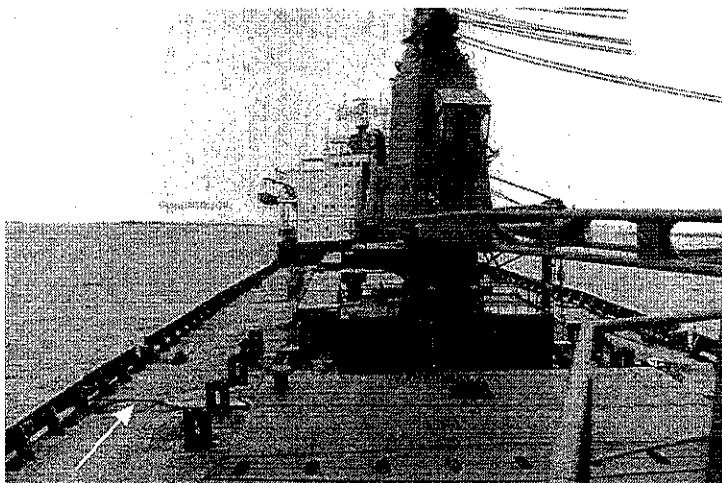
Emplacement de la fracture sur le pont principal (voir la flèche)
